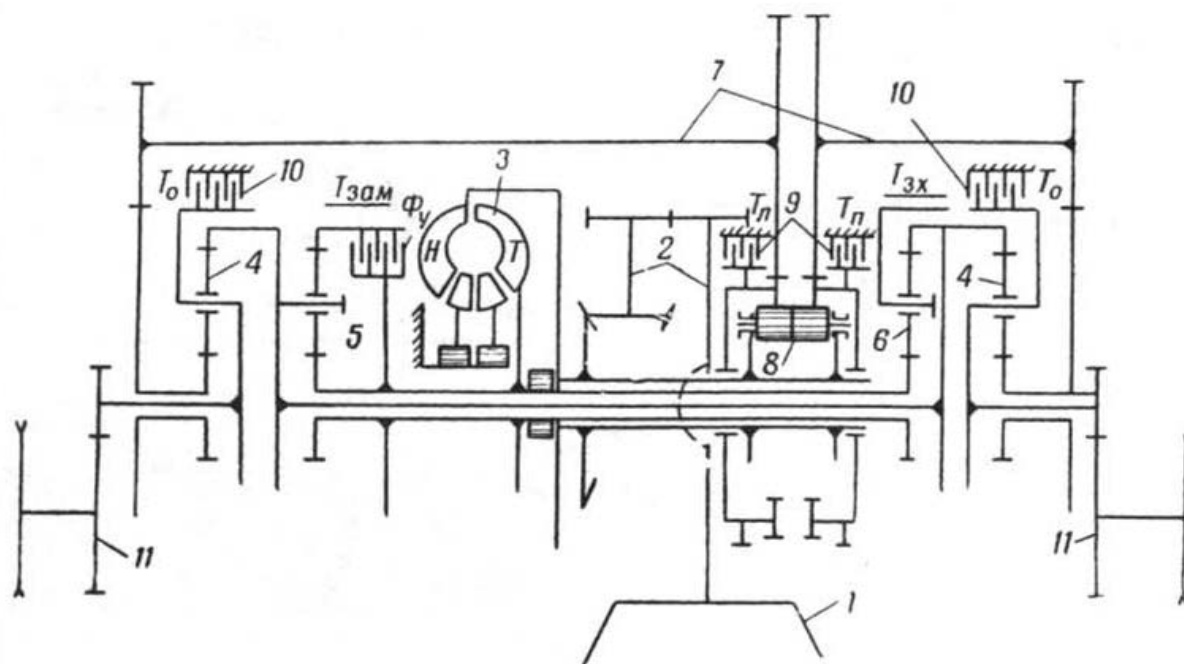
Принципиальная кинематическая схема гидромеханической трансмиссии «кросс-драйв»: 1 – двигатель; 2 – первичный редуктор; 3 – комплексный гидротрансформатор; 4 – суммирующие планетарные ряды; 5 – планетарный ряд замедленной передачи; 6 – планетарный ряд заднего хода; 7 – дополнительные передачи; 8 – простой цилиндрический дифференциал; 9 – тормоза поворота; 10 – остановочные тормоза; 11 – бортовые передачи.
